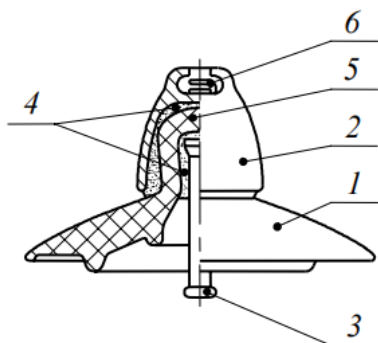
Підвісний шарнірний ізолятор із конусною головкою:
